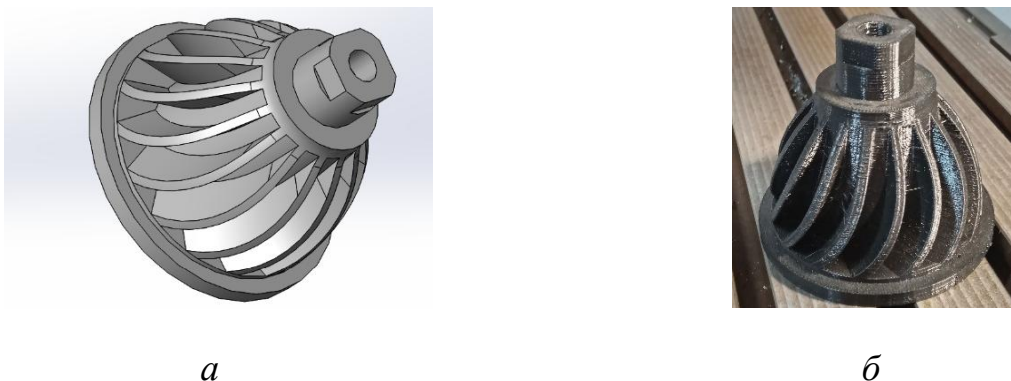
Загальний вигляд деталі: *а* – 3D-модель; *б* – деталь надрукована 3D-друком без оброблення
